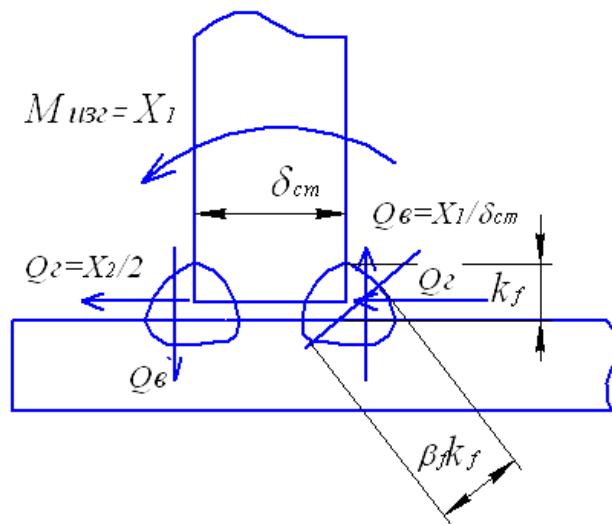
Расчетная схема для расчетного сварного шва
